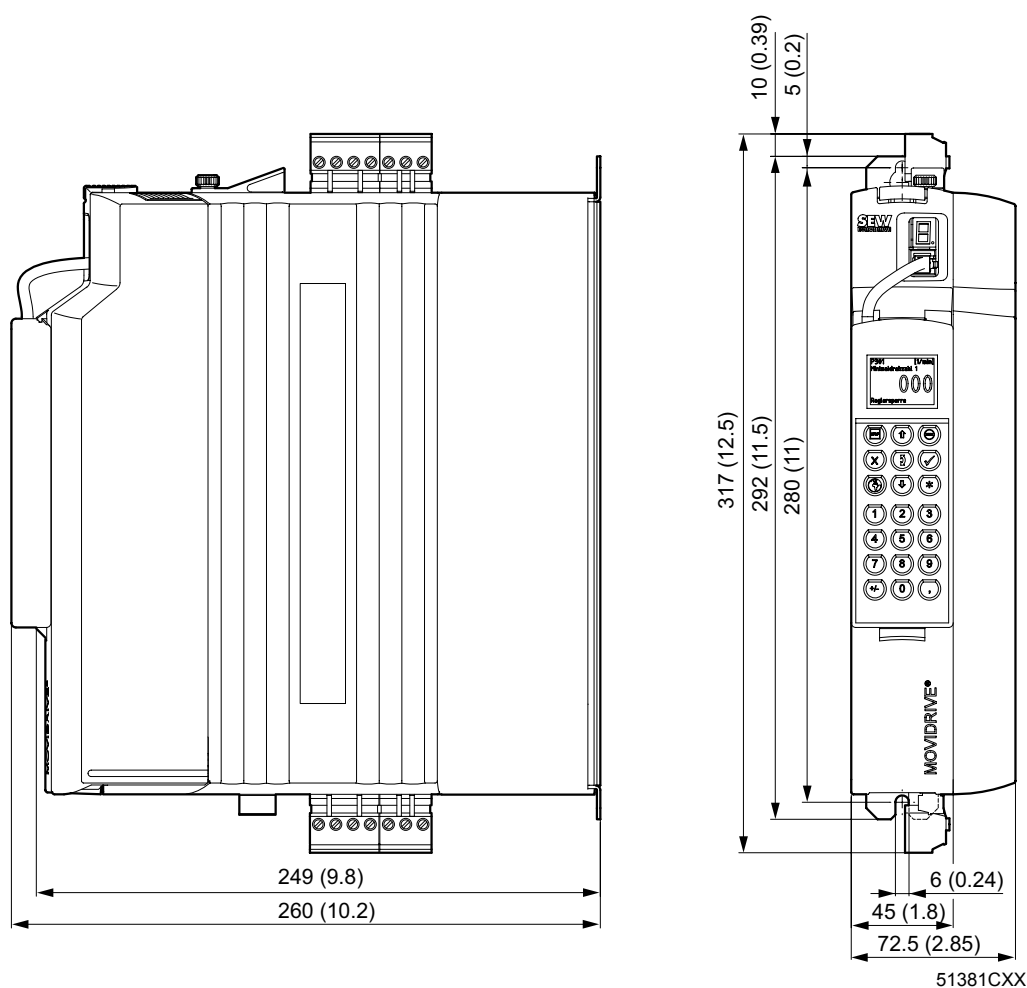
Dimensões MDX61B, tamanho 0S, dimensões em mm (in)
